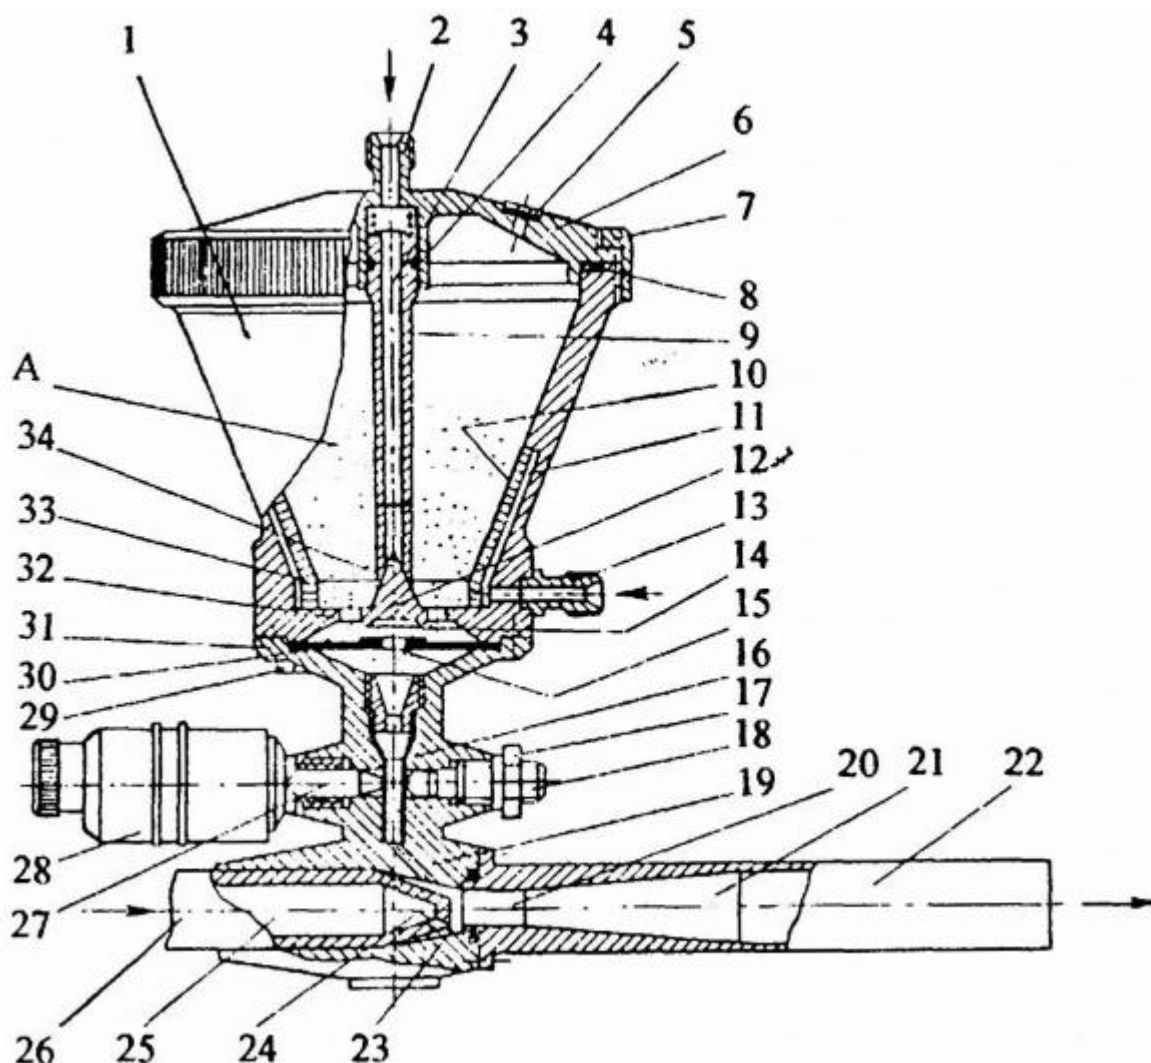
Схема інжекторного дозатора із аеруючими стінками: 1 бункер; 2 - вхідний штуцер; 3 - осьовий канал; 4 - ущільнення; 5 - патрубок; 6 - кришка бункера; 7 - гайка; 8 - ущільнення; 9 трубка; 10 - конус; 11 - кільцева порожнина; 12 зворотний центральний конус; 13 штуцер; 14 - сидло; 15 отвір; 16 -еластична трубка; 17 -гайка; 18 - жиклер; 19 ~ підвідний канал; 20 - циліндрична ділянка патрубка 22; 21 - дифузор; 22 - патрубок; 23 - порожнина змішування; 24 - крівні отвори; 26 - канал; 26 - сопло; 27 - шток; 28 ~ клапан; 29 - гвинт; 30 мембрана. 31 корпус; 32 - решітчаста перегородка; 33 - аеруючі стінки; 34 радіальні отвори; А порошок.
